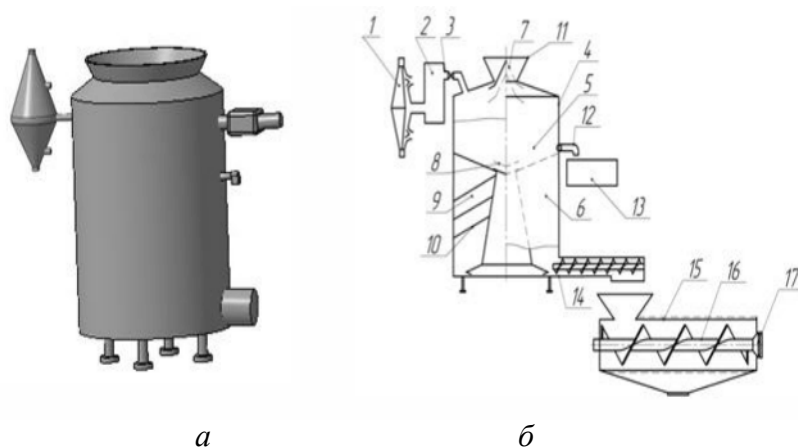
Схема установки для измельчения растительного сырья: 1 - компрессор; 2 - подогреватель воздуха; 3 - подводящие трубы; 4 - корпус; 5 - компрессионная камера; 6 - декомпрессионная камера; 7 - затвор; 8 - перепускное устройство; 9 - регрессивный циклон; 10 - спиральные полки; 11 - загрузочное устройство; 12 - отводящий желоб; 13 - ёмкость; 14 - выгрузное устройство; 15 - зерновая камера пресса; 16 - шнек; 17 - затворное устройство
